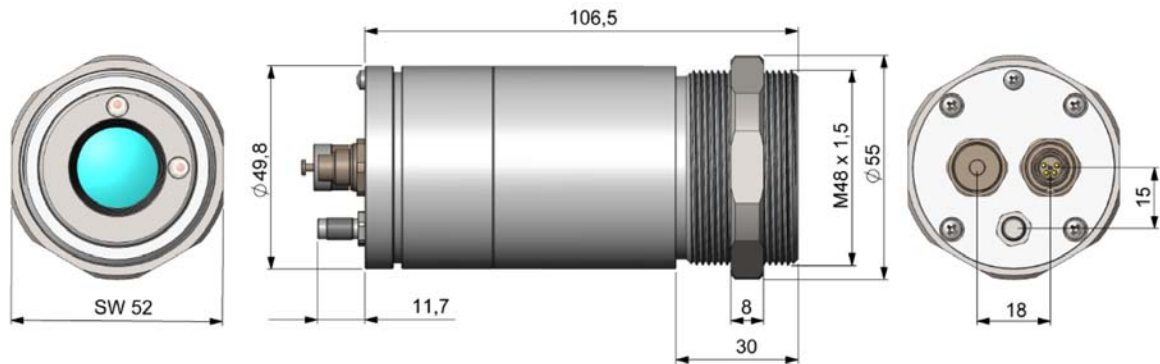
Maßzeichnung thermoMETER CTVideo-Sensor (Hochtemperaturversion)
